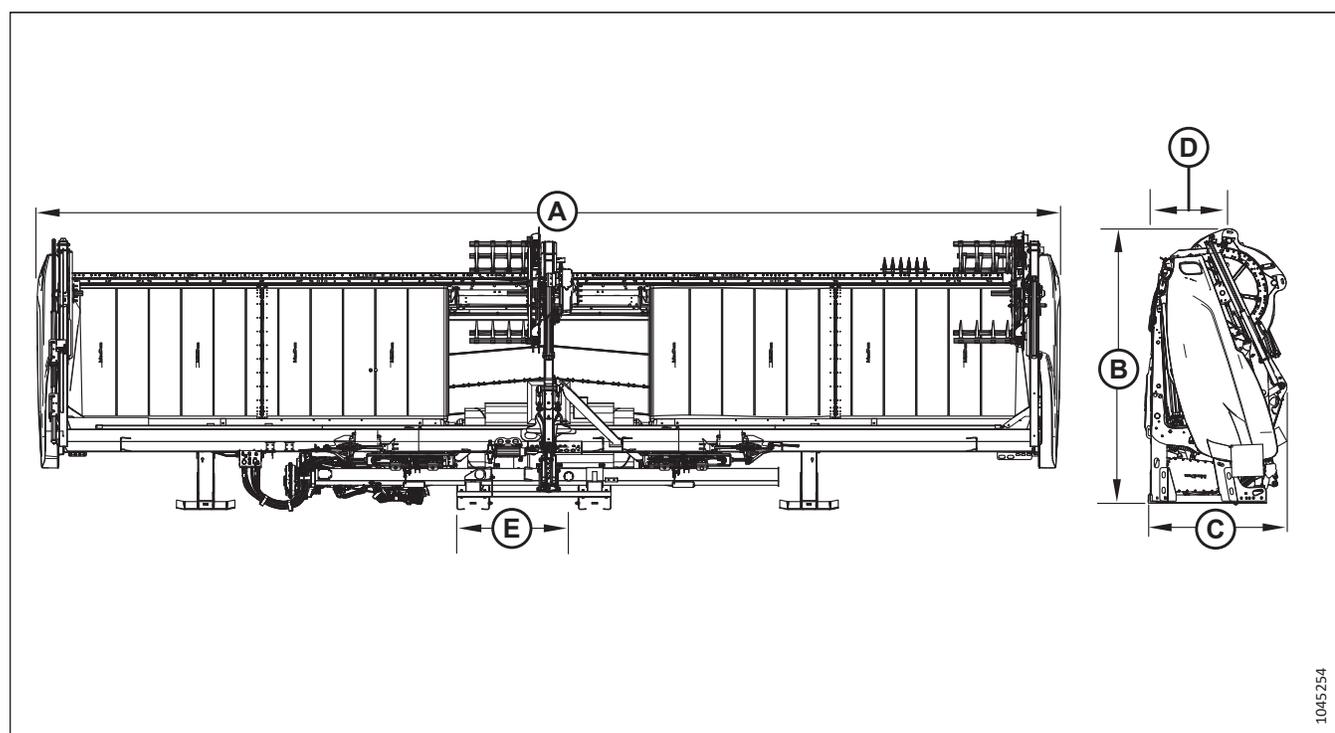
Plateforme entièrement assemblée et fixée aux supports d'expédition
